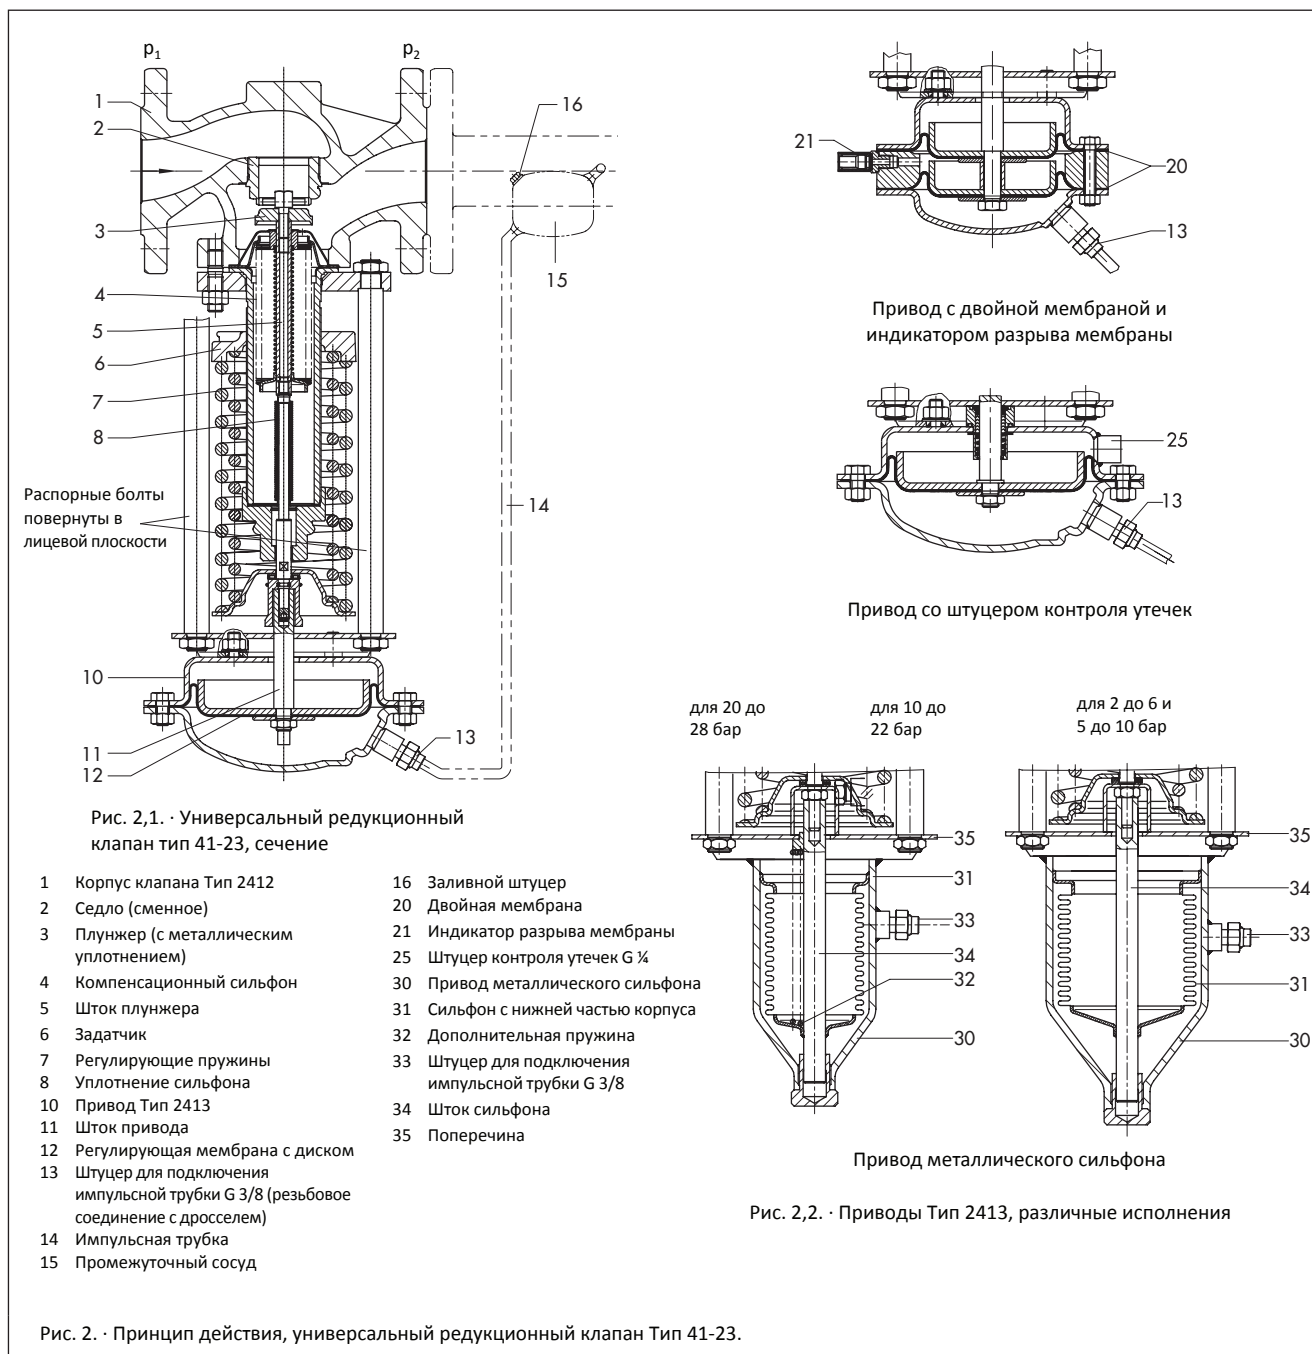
Принцип действия, универсальный редуцирующий клапан Тип 41-23.
